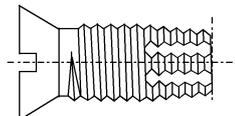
Gewinbeschneidende Schraube (siehe 3.19)
